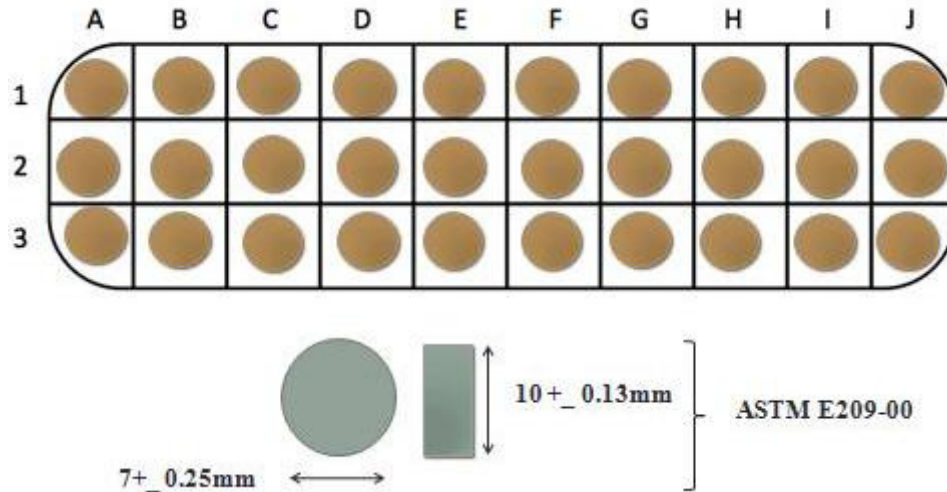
Esquema del maquinado de las probetas y sus dimensiones
